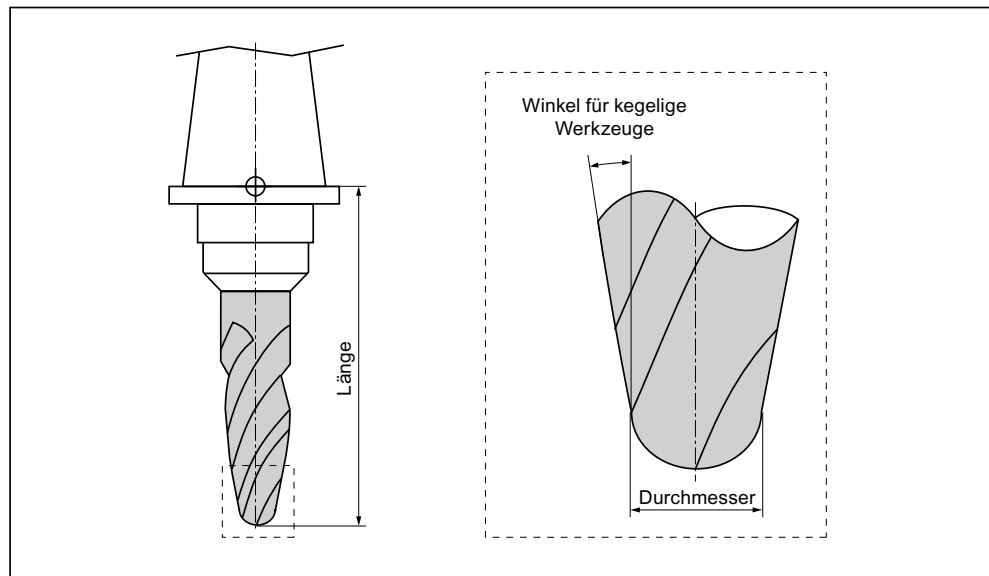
3D-Werkzeug am Beispiel eines kegigen Gesenkräfers (Typ 157)
